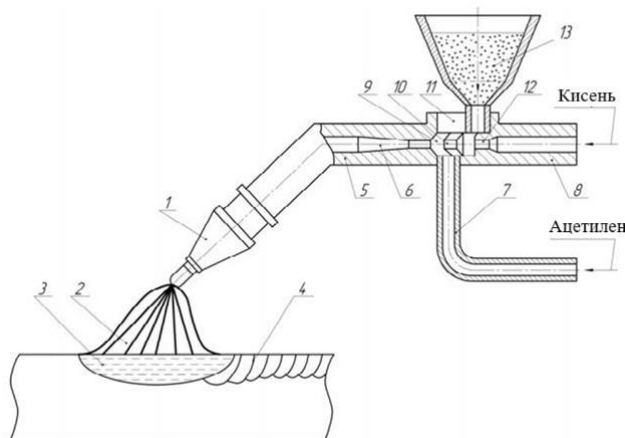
Схема газопорошкового напилення порошку: 1 – мундштук; 2 – полум'я; 3 – зварювальна ванна; 4 – наплавлений шар; 5 – трубка; 6 – канал; 7 – ацетиленова трубка; 8 – киснева трубка; 9 – камера змішування; 10, 12 – ейектори; 11 – змішувальна камера; 13 – порошок.
